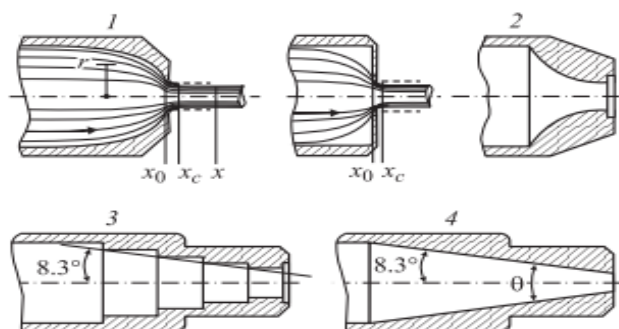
Внешние сходящиеся насадки (1-насадок с возрастающей к выходу кривизной профиля; 2 – насадок короткий конoidalный; 3 – ступенчатый насадок; 4 – конический) насадок
